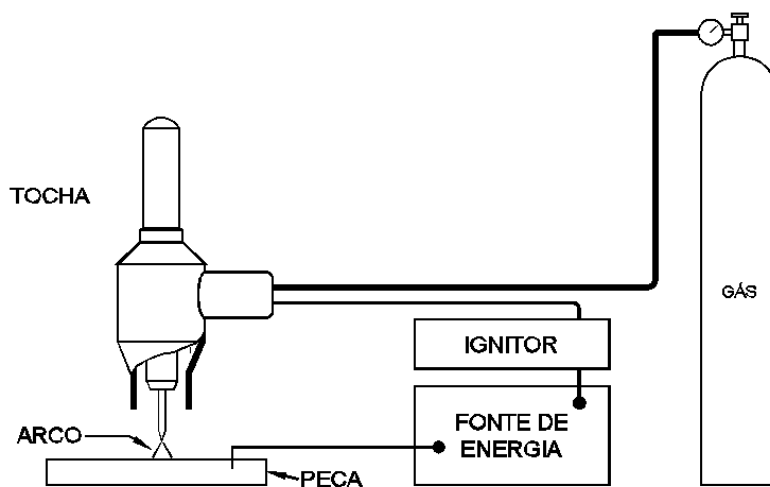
Equipamento para soldagem TIG (esquemática). Baseado em <sup>[1 e 2]</sup>
